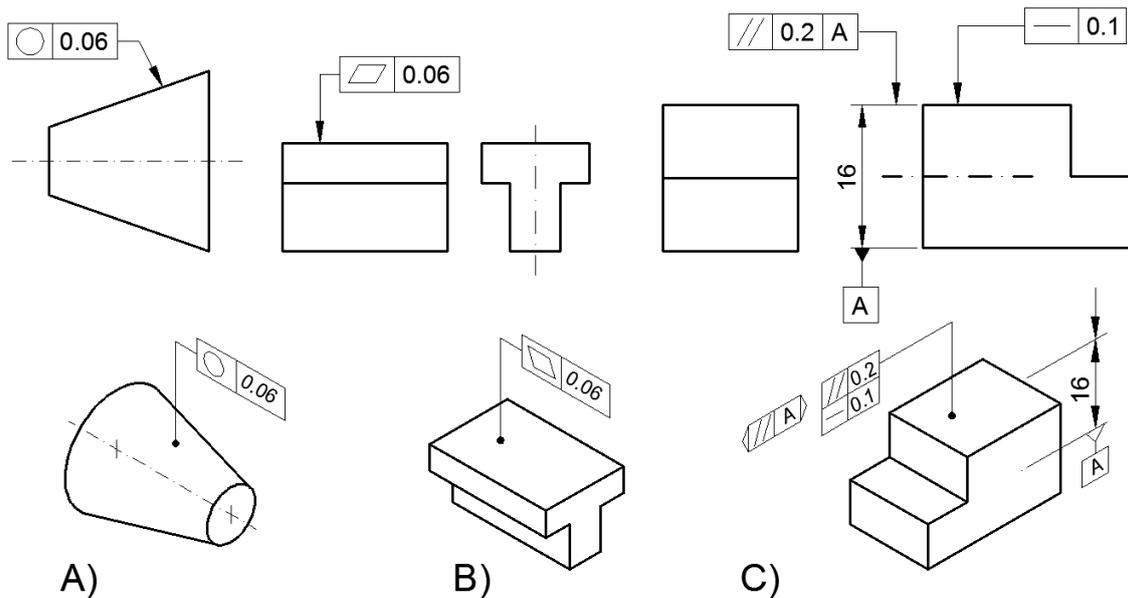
Acotación de tolerancias geométricas. Superficies.
